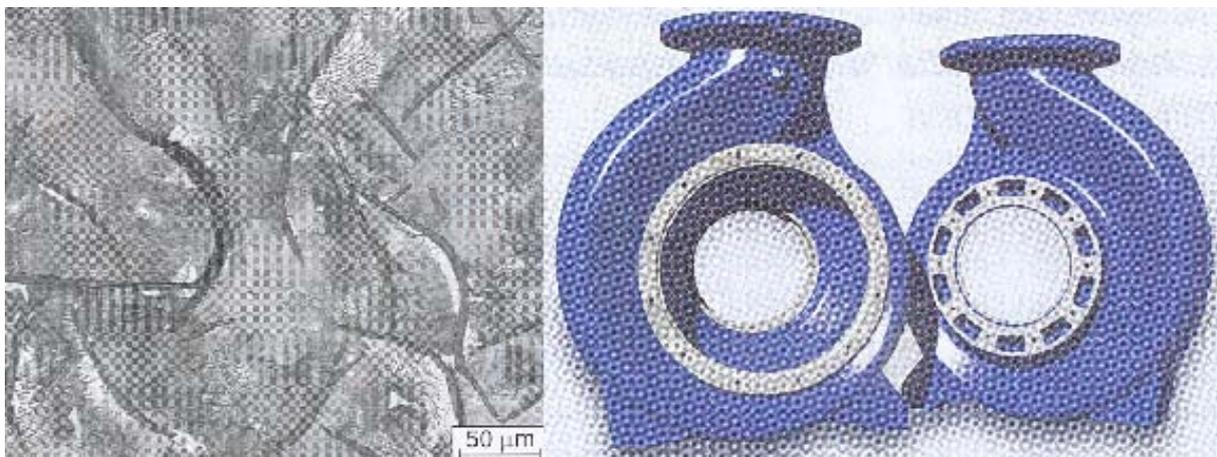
Gusseisen mit Lamellengraphit: links: Gefüge [2]; rechts: Gehäuse für Umwälzpumpen (Herborner Pumpenfabrik J. H. Hoffmann, Herborn) [2]
